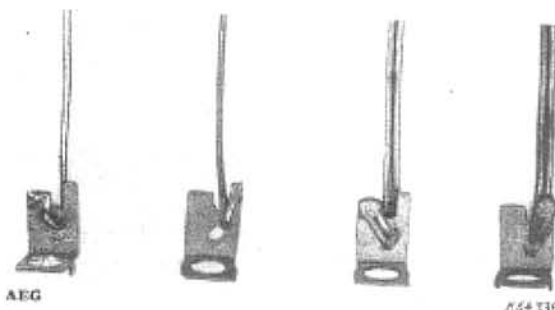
Schweißung von Kupferdrähten an messingplattierte Eisenösen.
